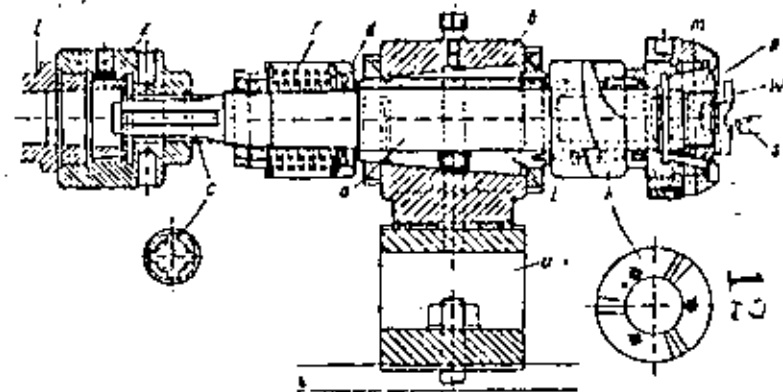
Dispositivo para torneado de garras de acoplamiento
